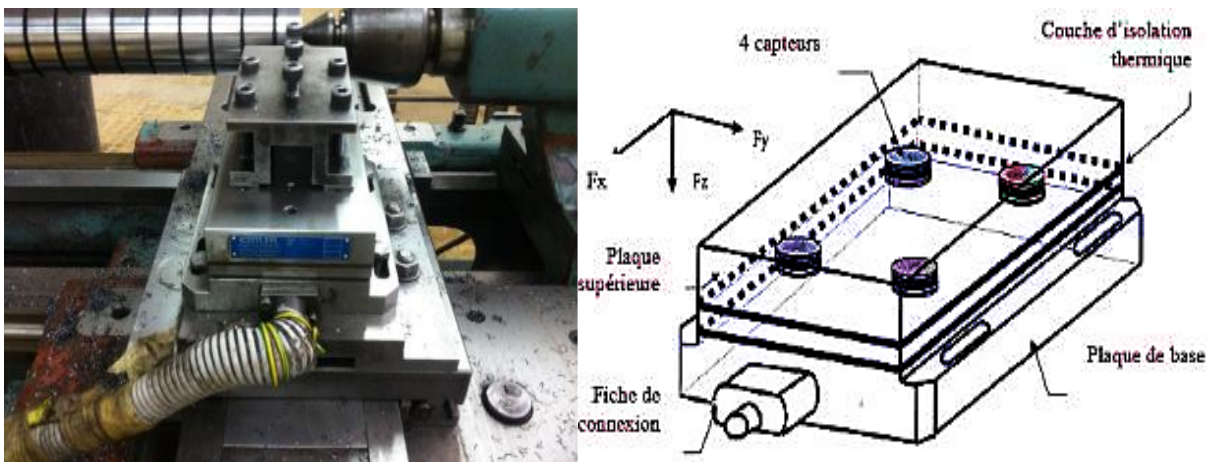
Capteur d'effort de coupe KISTLER [13].
